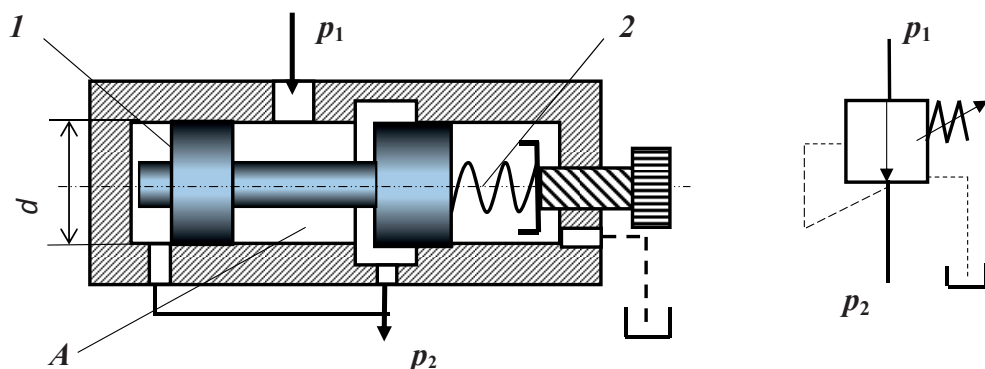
Конструктивная схема и обозначение редукционного клапана
